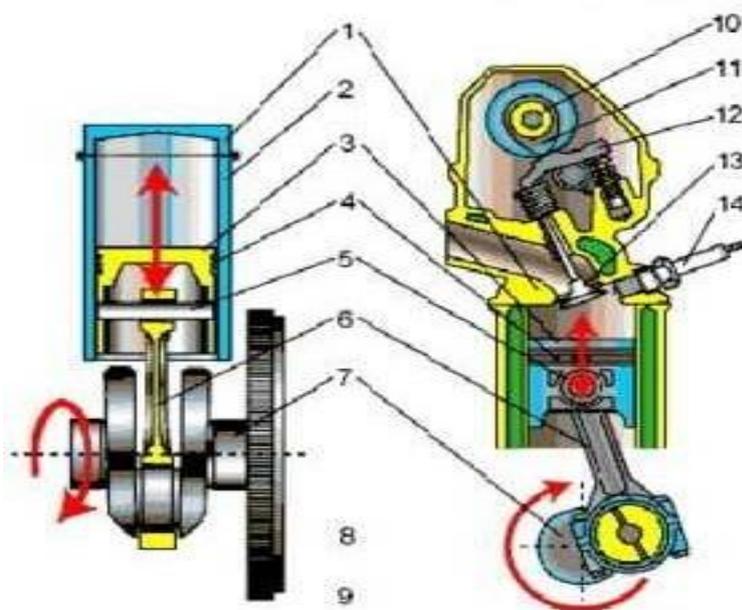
Схема конструкции двигателя внутреннего сгорания в продольном и поперечном разрезе:
